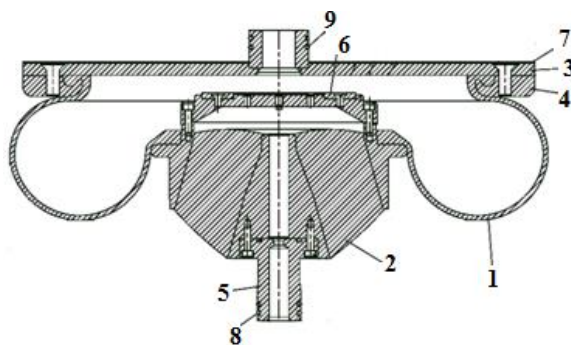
Пневматична ресора 1Ао90-1к швидкісного електропоїзда «Hyundai Rothem»: 1 – пневматична ресора; 2 – конічний гумометалевий амортизатор; 3 – верхня пластина; 4 – кільце; 5 – штифт; 6 – пластина; 7 – гумова пластина; 8, 9 – ущільнююче кільце
